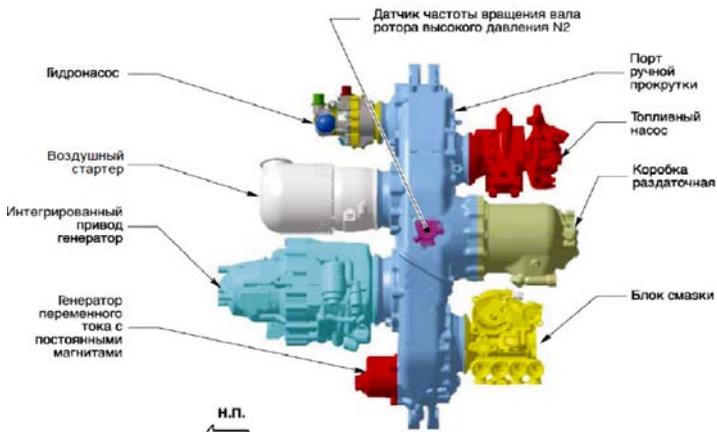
Агрегаты, размещенные на коробке приводов
